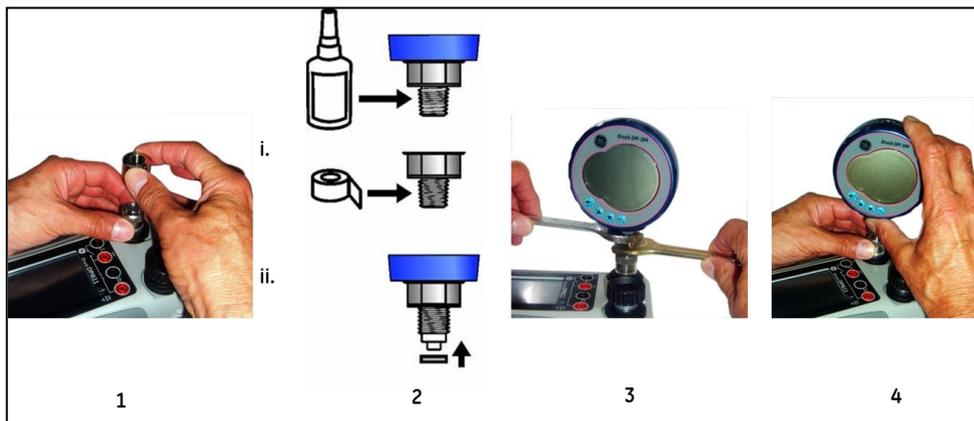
Collegamento/Rimozione dei collegamenti di pressione
